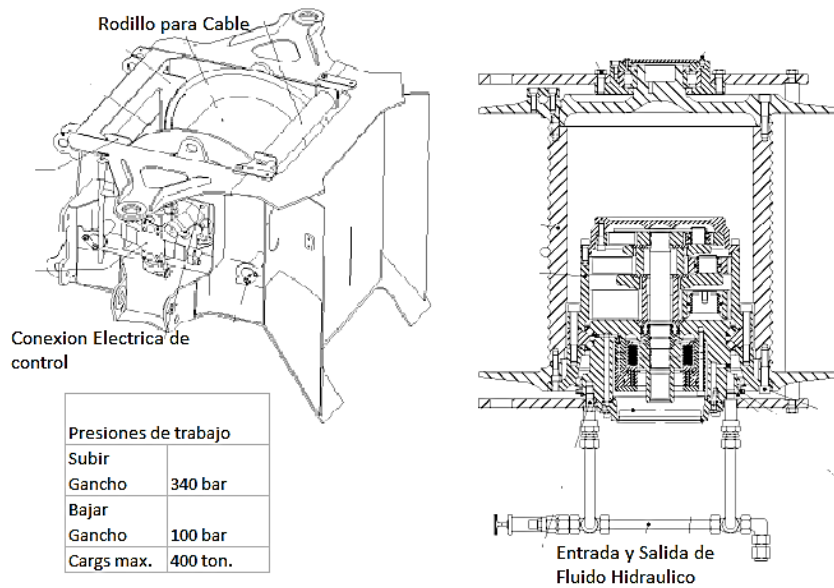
Cabestrante de elevación- imagen en corte.
